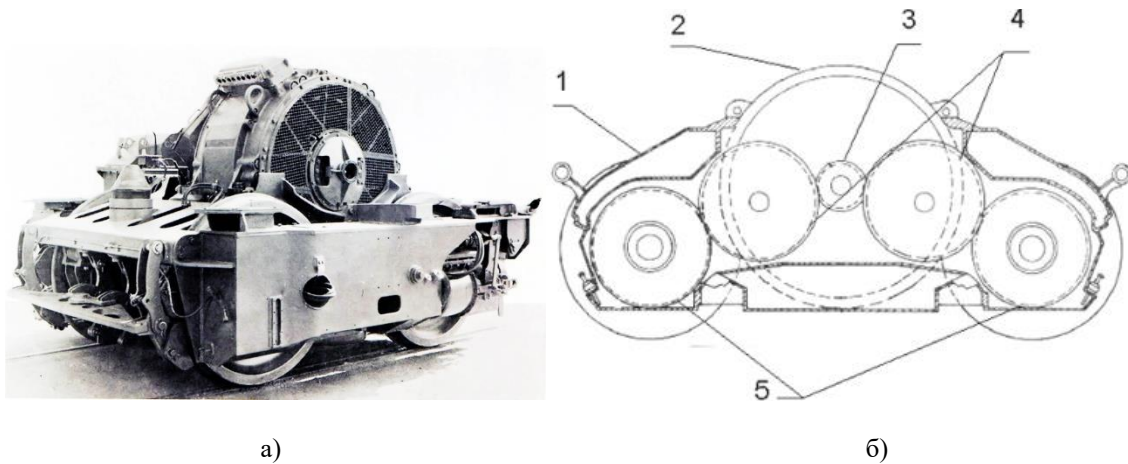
Двовісний монотворний візок електровозу BB16500, а) – загальний вигляд візка б) – схема приводу колісних пар візка: 1 – корпус редуктора, 2 – тяговий електродвигун, 3 – привідна шестерня, 4 – проміжні («паразитні») зубчасті колеса, 5 – зубчасті колеса колісних пар
